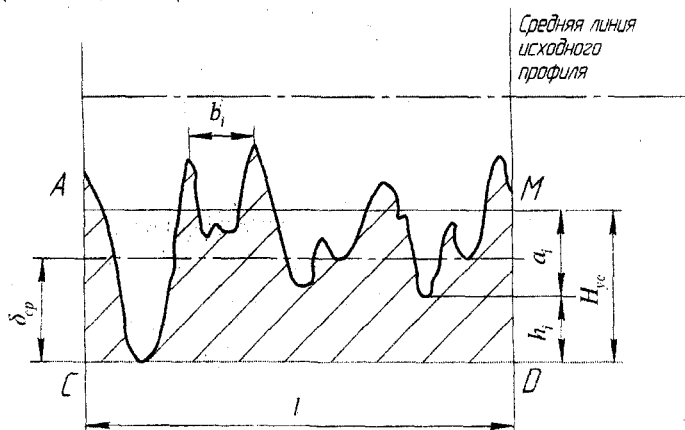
Схема образования профиля шероховатости поверхности при обработке свободными абразивами
